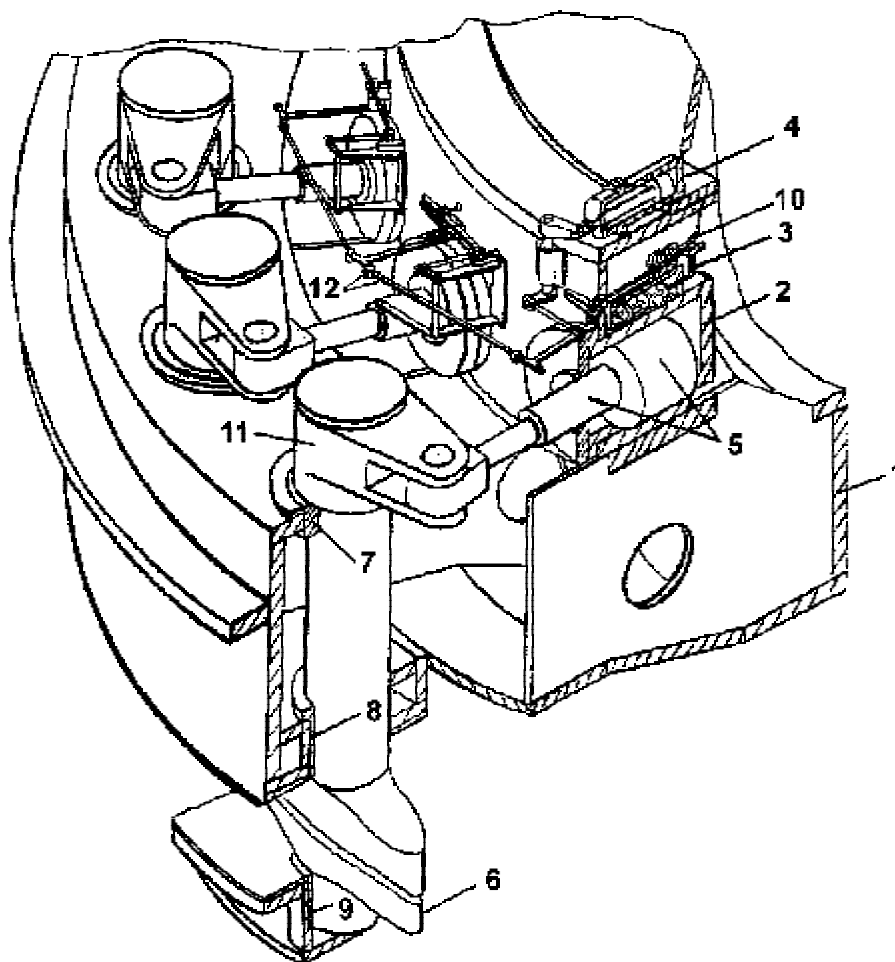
Крышка турбины в сборе с опорой подпятника и индивидуальными сервомоторами привода лопаток направляющего аппарата Саяно-Шушенской ГЭС
